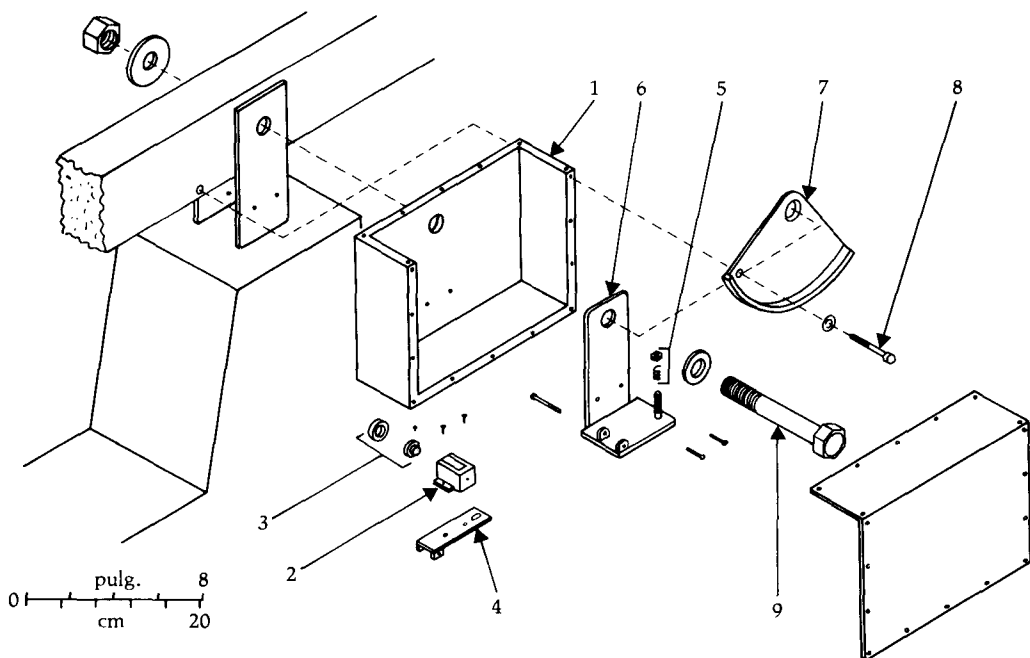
Diseño del montaje para el contador mecánico: (1) caja o cárter; (2) contador; (3) rueda del contador y anillo de caucho; (4) sostén del contador; (5) tuerca de ajuste y resorte del contador; (6) montaje de guía (7) balancín; (8) eje del balancín; y (9) pasador de la manija de la bomba.
